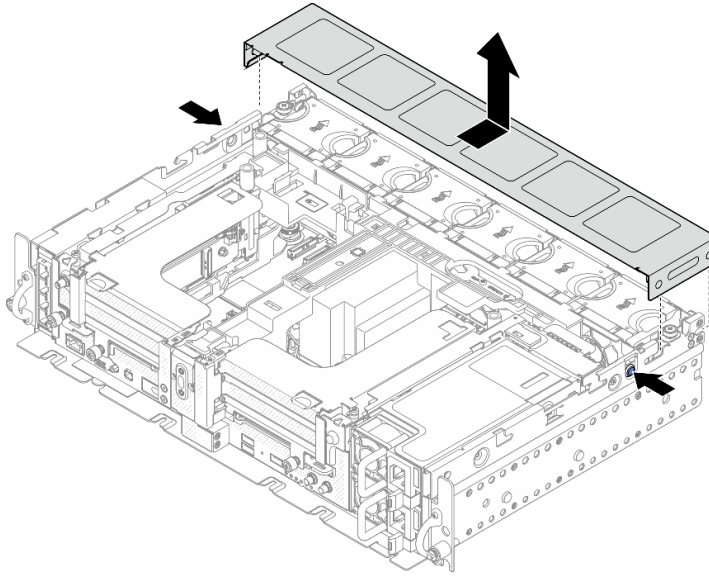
Extracción de la cubierta del ventilador (300 mm)
